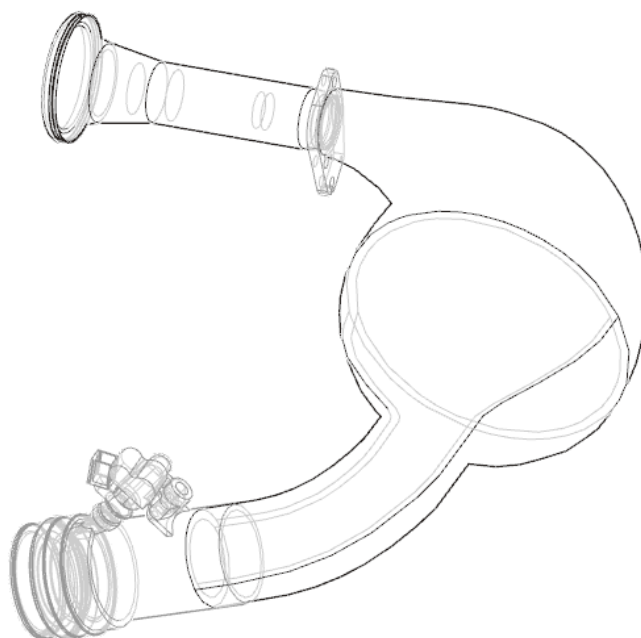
Корпус форсунки гоночного болида класса «Формула Студент»
